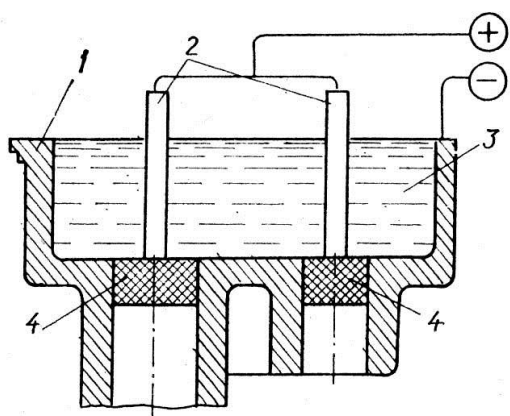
Схема електролітичного нарощування внутрішньої поверхні корпусу насоса:
